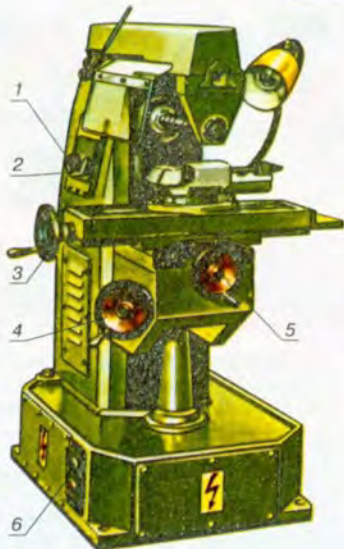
Розташування органів керування горизонтально-фрезерним верстатом НГФ-110 Ш4:
